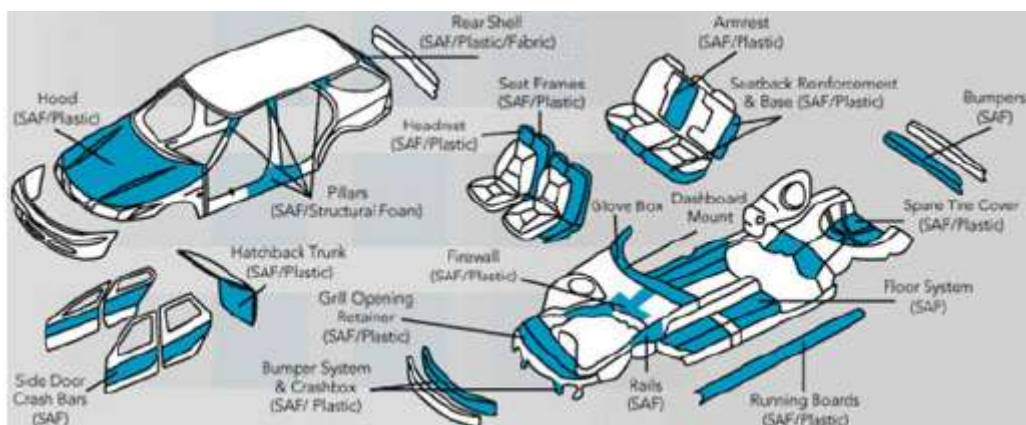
Aplicação de espumas metálicas no design automotivo. (Eduardo Cardoso)
